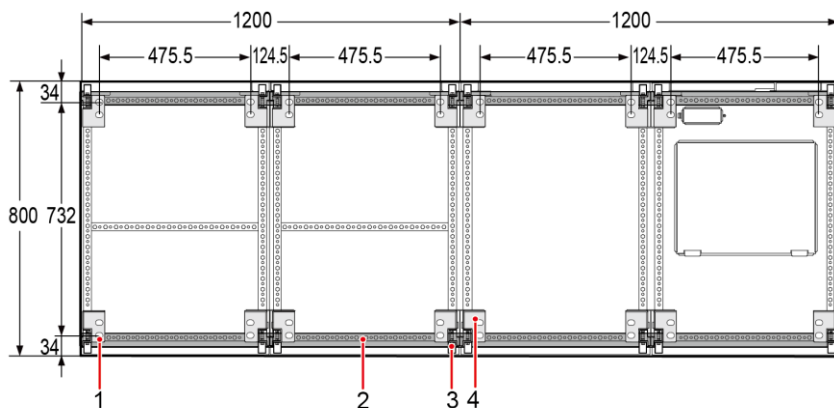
机柜底座安装孔尺寸图 (600kVA, 单位: mm)
